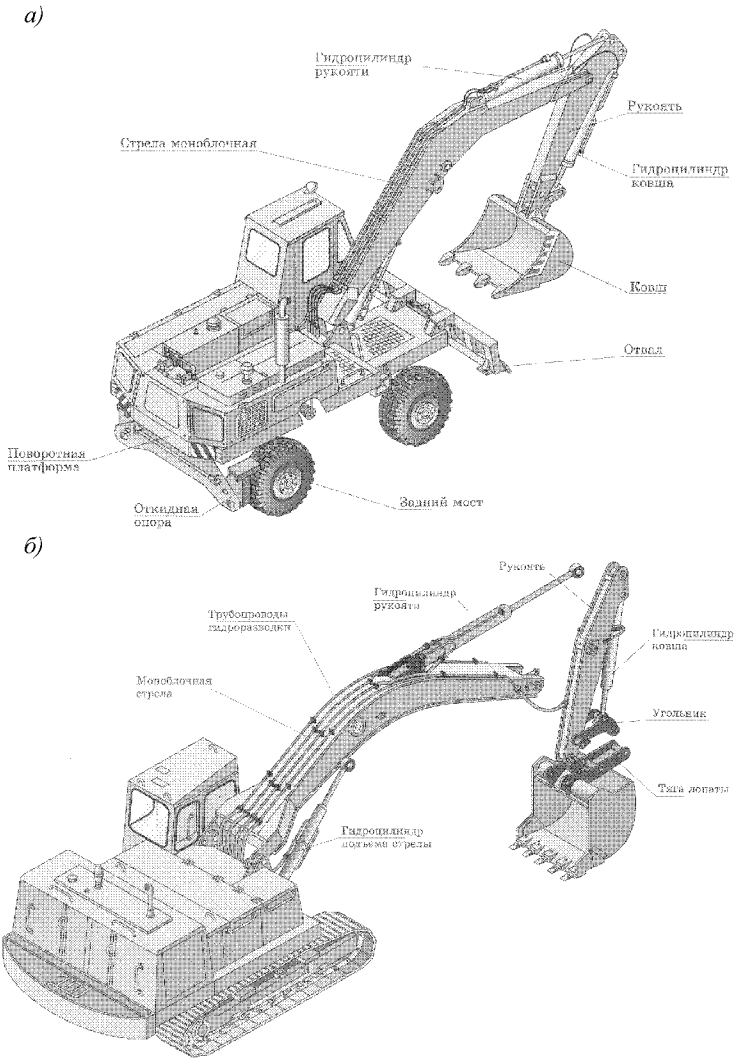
Гидравлический полноповоротный одноковшовый экскаватор:
